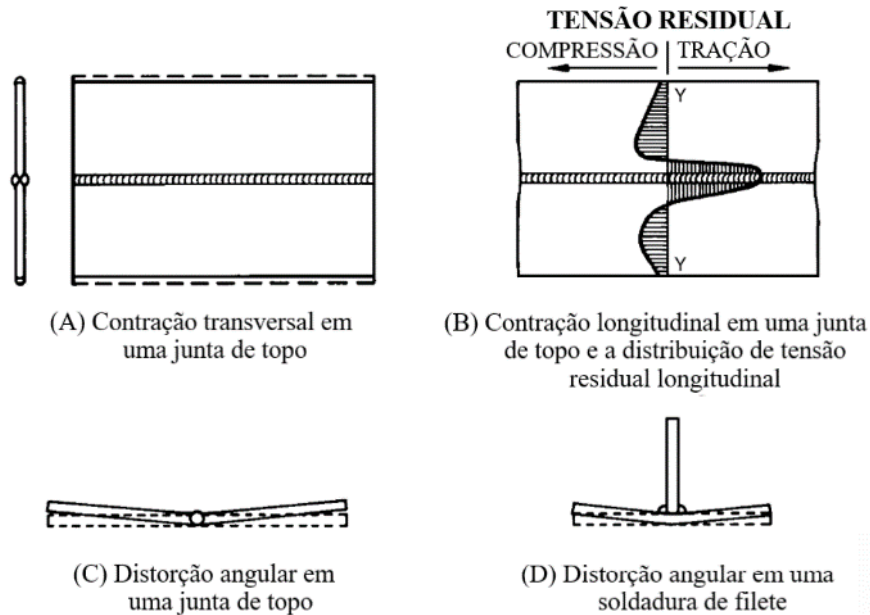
Variações dimensionais fundamentais que ocorrem em soldaduras. Adaptado de [23]
